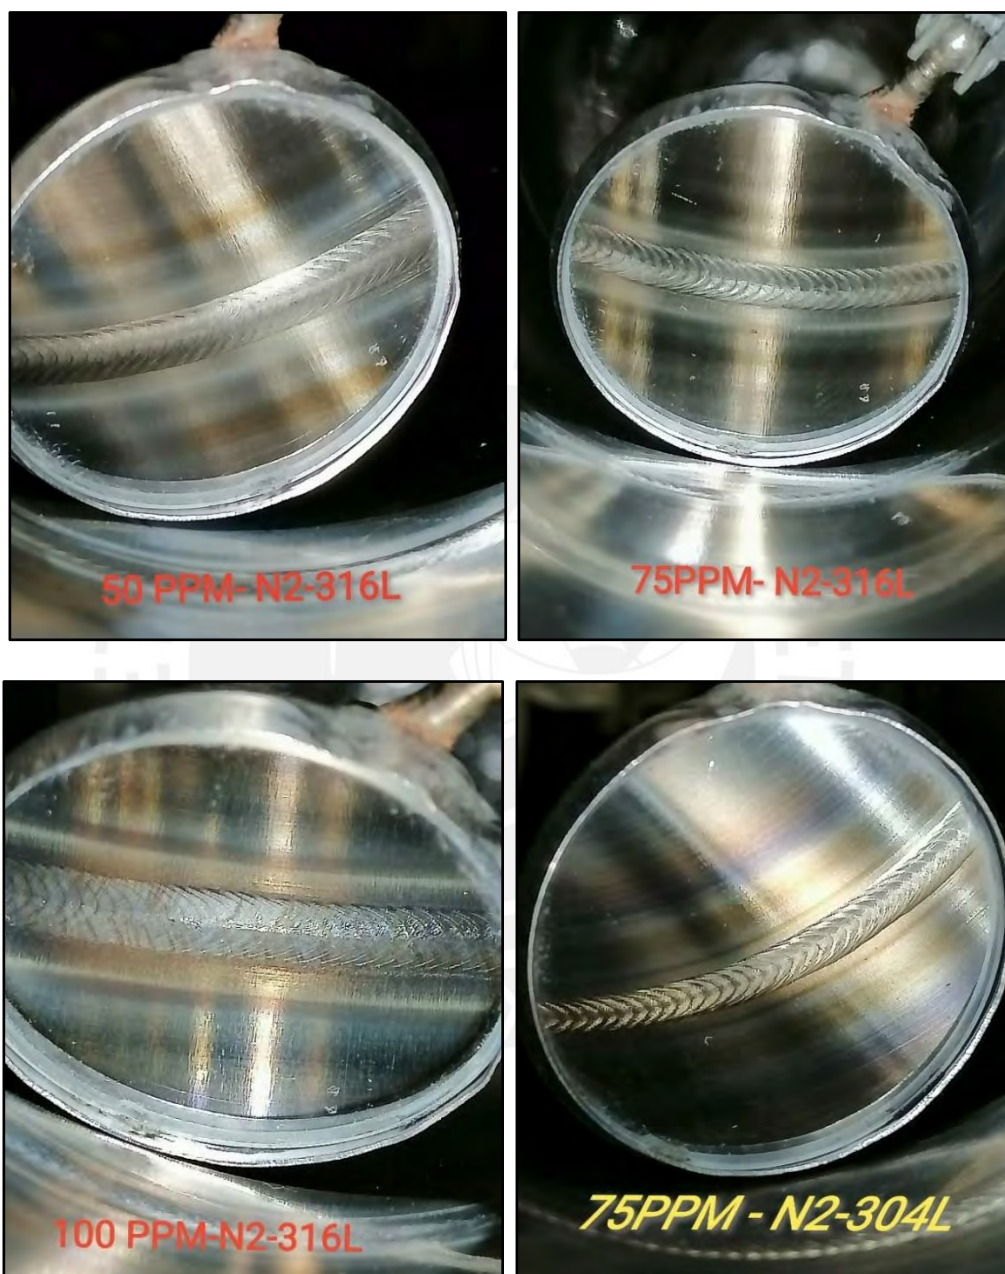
Inspección visual de la raíz en la zona de fusión para diferentes condiciones de soldadura.
